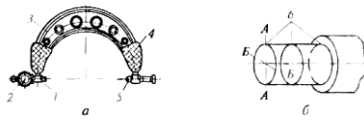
Скоба с отсчетным устройством (а) и определение посадочных размеров конца вала (б): 1 и 5 — подвижная и переставная пятки; 2 — отсчетное устройство; 3 — корпус; 4 — теплоизоляционная накладка; б — места измерений
